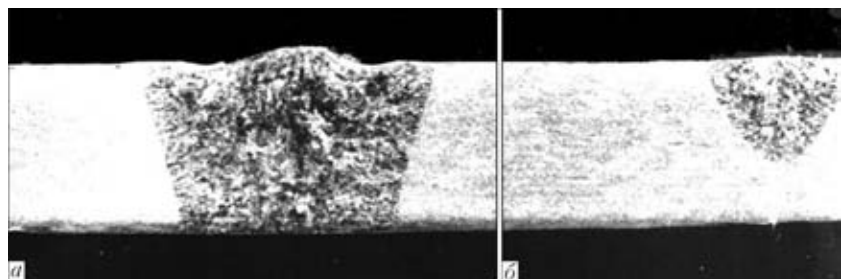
Макроструктуры наплавки на титановом сплаве ВТ1 ($\delta = 10$ мм): а — лазерно-дуговая сварка; б — лазерная сварка
